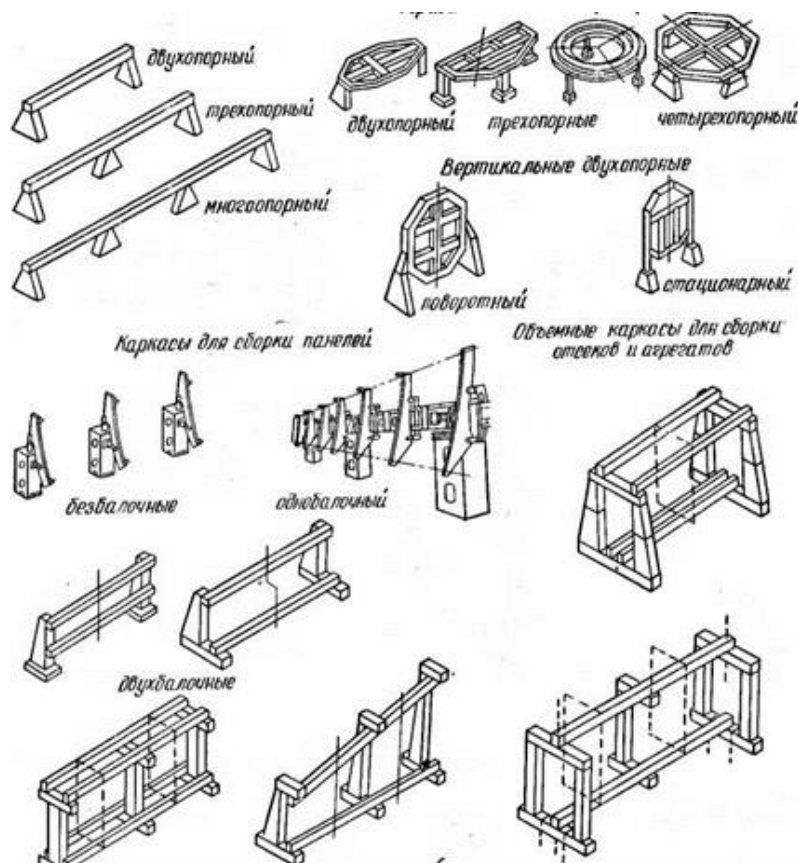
Типовые конструкции каркаса сборочного приспособления
